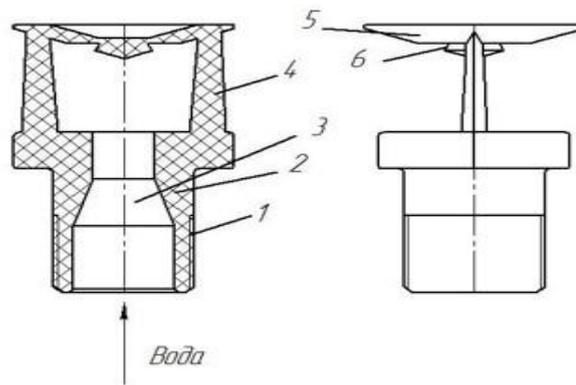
Дождевальная дефлекторная насадка с канавкой: 1 – резьба; 2 – корпус; 3 – сопло; 4 – ножка дефлектора; 5 – дефлектор; 6 – канавка.
